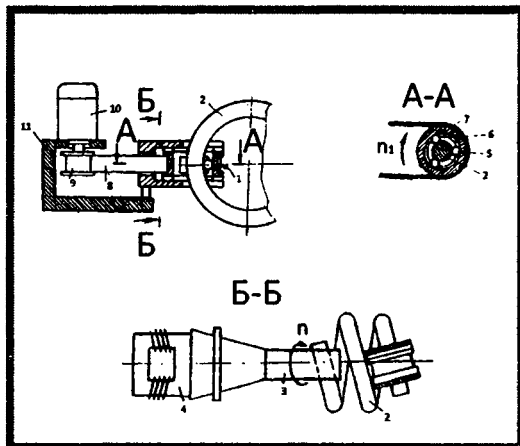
Схема устройства для упрочняюще-чистой обработки деталей типа винтовых пружин
